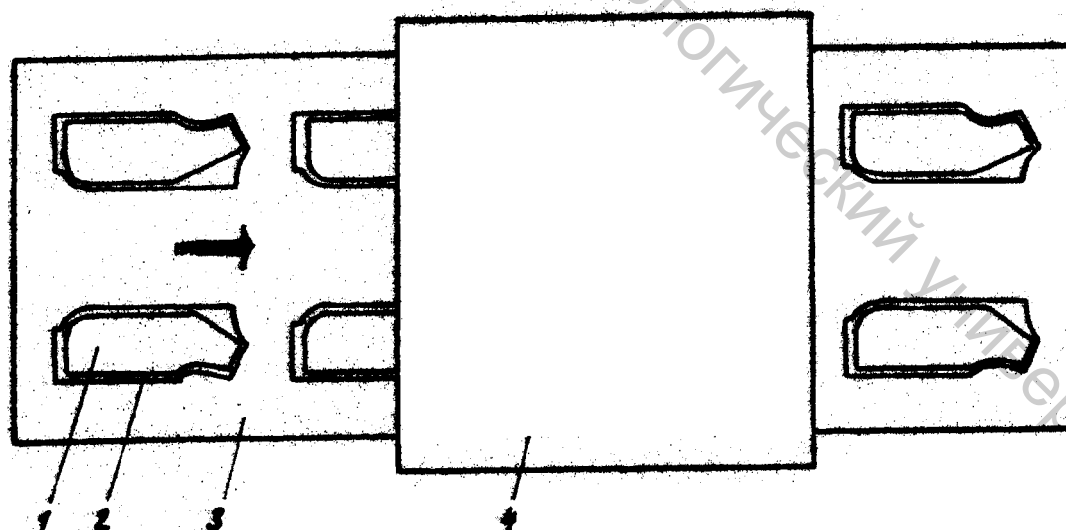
Схема укладки и размещения деталей на прессах с ограни-чением ленты транспортера с обеих сторон: 1-датчик из термоклеевого прокладочного материала; 2-деталь из основного материала; 3-лента транспортера; 4-зона нагрева и сжатия
